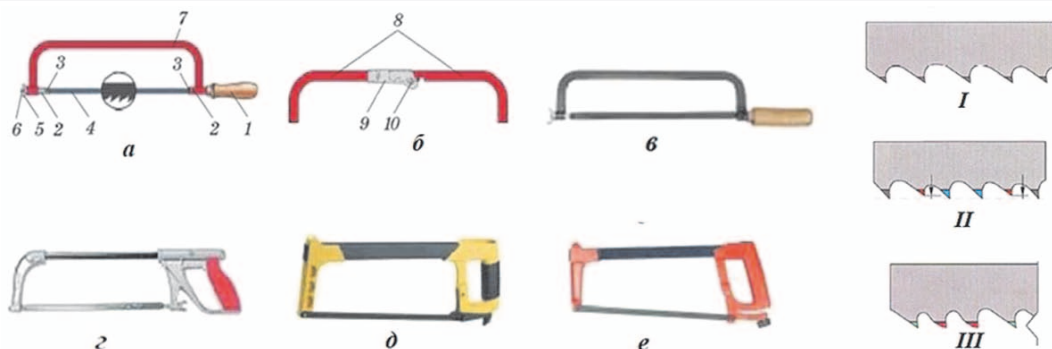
Будова і види ручних ножіврк: а — будова ножіврки з цілісною рамкою; б — будова ножіврки з розсувною рамкою: 1 — ручка, 2 — головка натяжного гвинта, 3 — штифт, 4 — пиляльне полотно, 5 — гайка-баранчик, 6 — гвинт натяжний, 7 — рамка, 8 — вугільник, 9 — планка, 10 — штифт-заклепка; в — ножіврка з цілісною рамкою; г, д, е — ножіврки з розсувною рамкою; I, II, III — приклади розводки зубів пиляльного полотна: I — стандартна, II — з розподіленою шириною пропилу, III — гібридна
